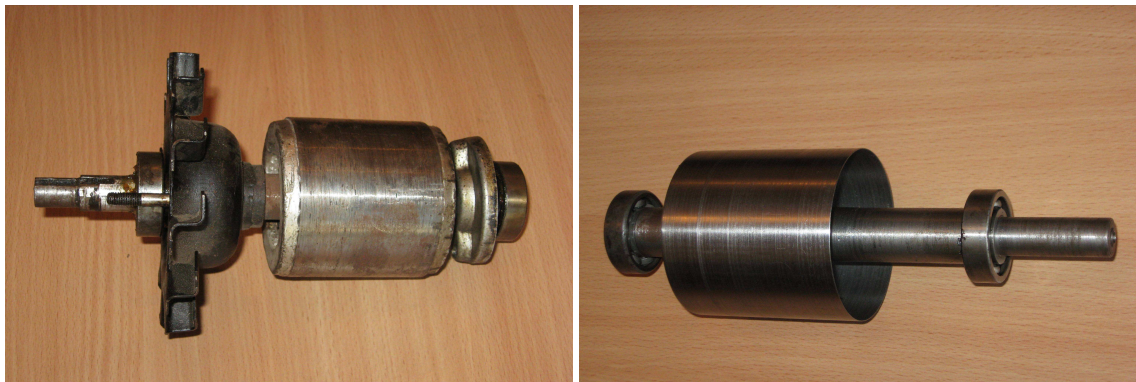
Ротор двигателя стандартный и исследуемый
